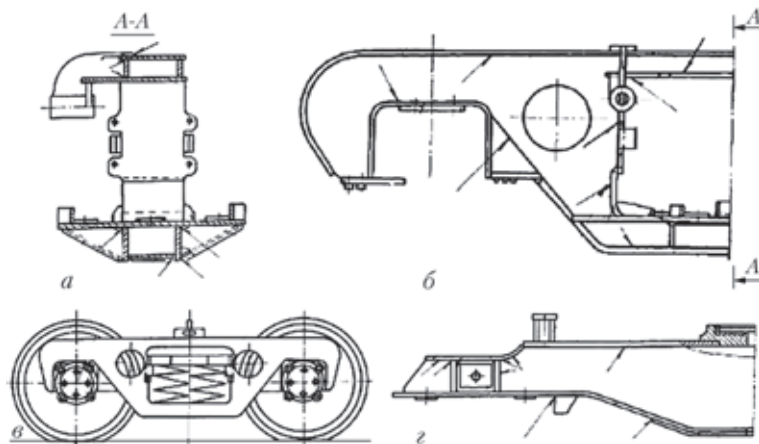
Схема сварной конструкции тележки грузовых вагонов «Крюковско-го вагоностроительного завода» [8]: *а* — разрез боковой рамы по оси симметрии; *б* — боковая рама; *в* — тележка; *г* — надрессорная балка
